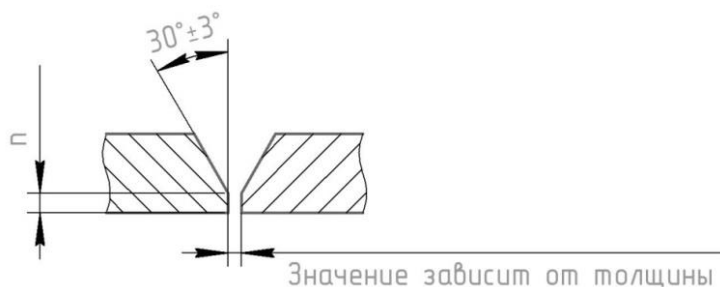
Конструктивные элементы подготовленных кромок стыкового сварного соединения
